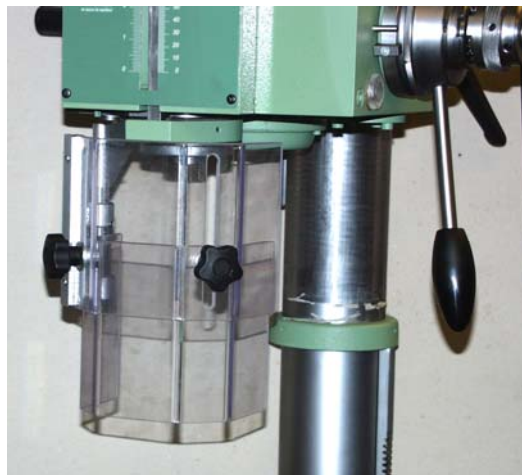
Borrar skydd – Picture 1. Drill guard – Abb. 1. Bohrschutz
